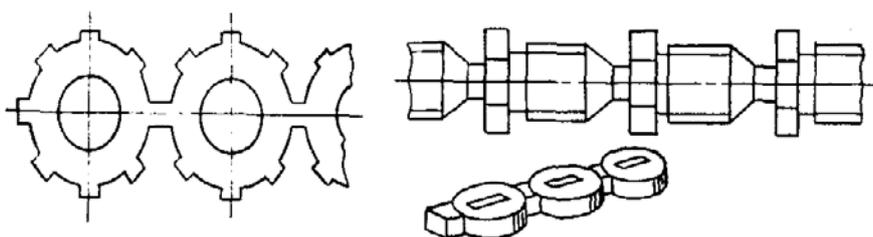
Усовершенствованные конструкции присоединяемых деталей для подачи на сборку
